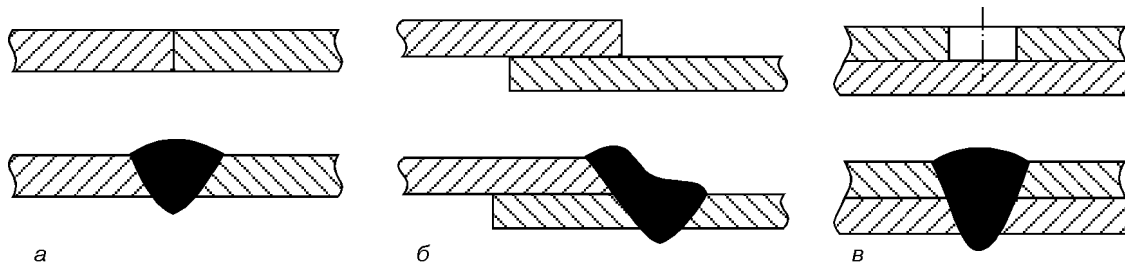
Подготовка кромок и типы соединений: а — стыковое, б — нахлесточное; в — с отверстием в одном листе
